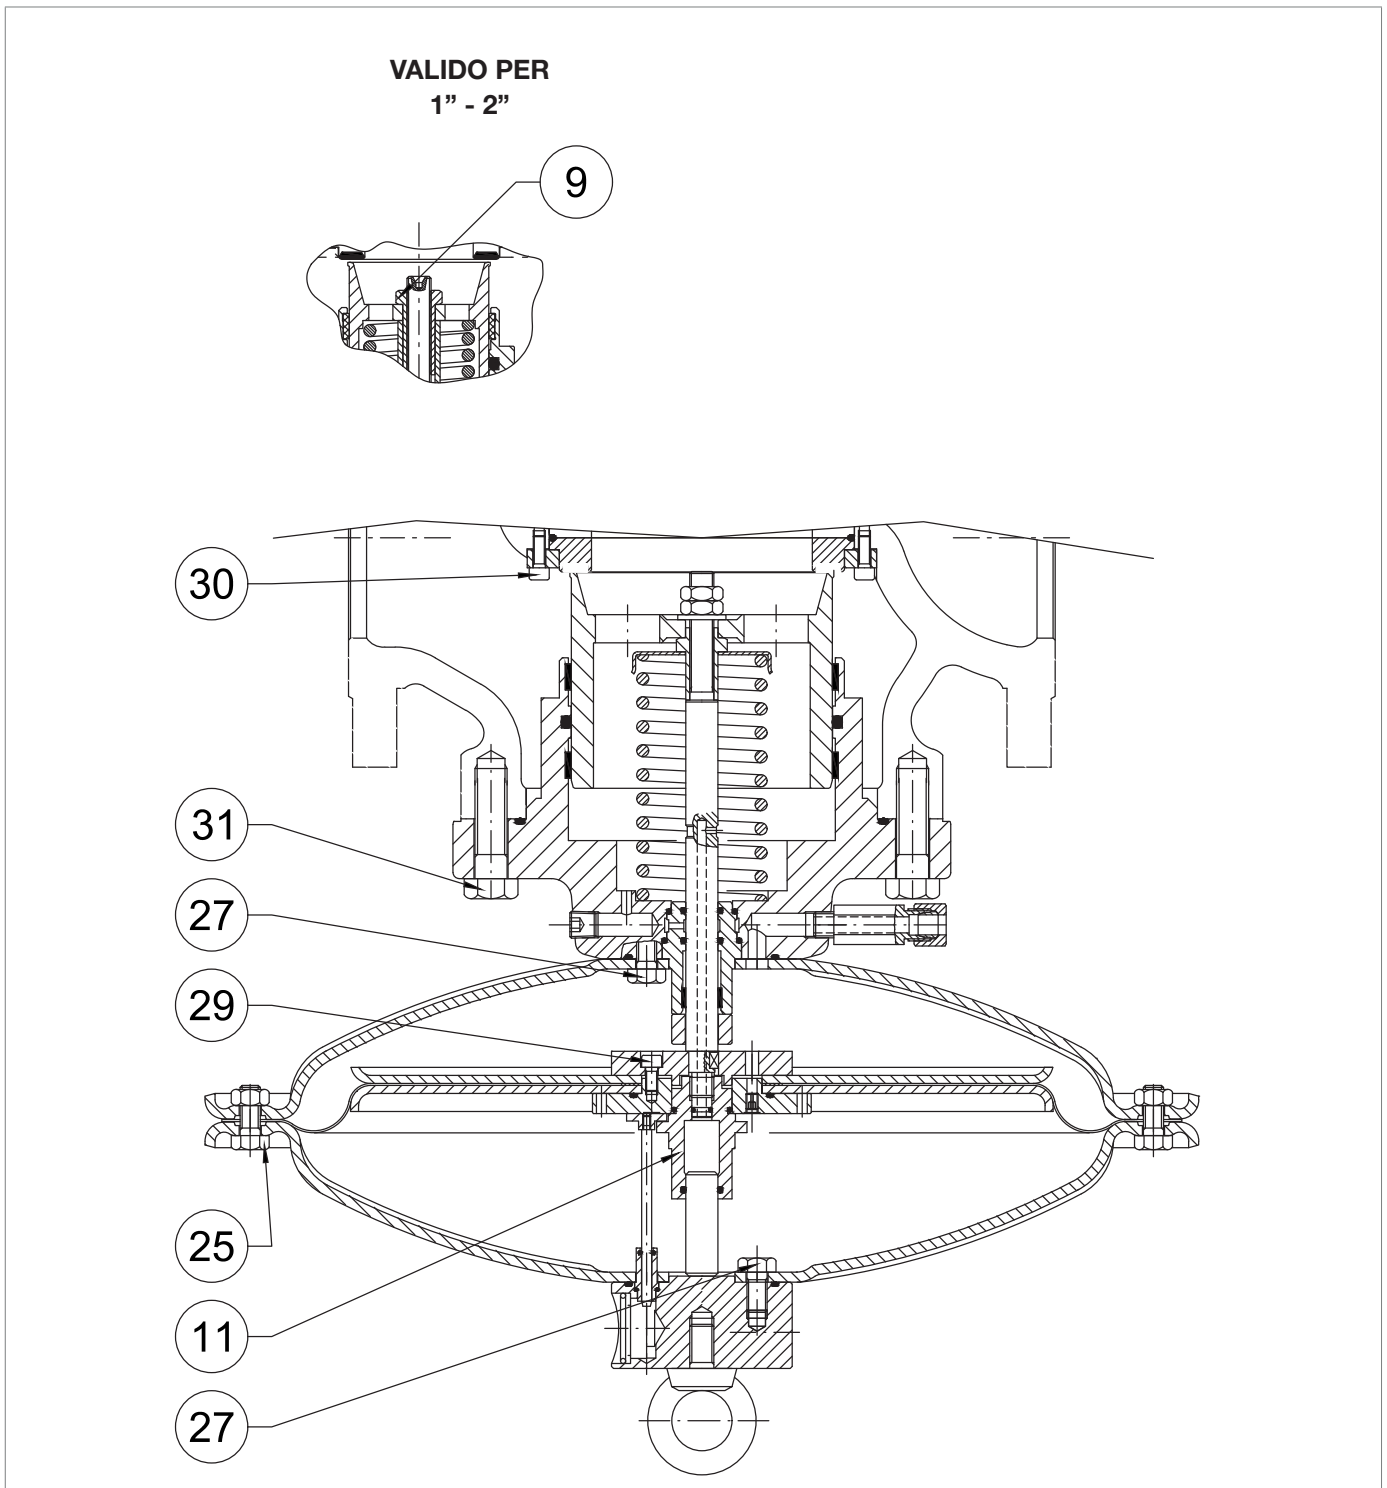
Coppie di serraggio monitor incorporato PM/182
